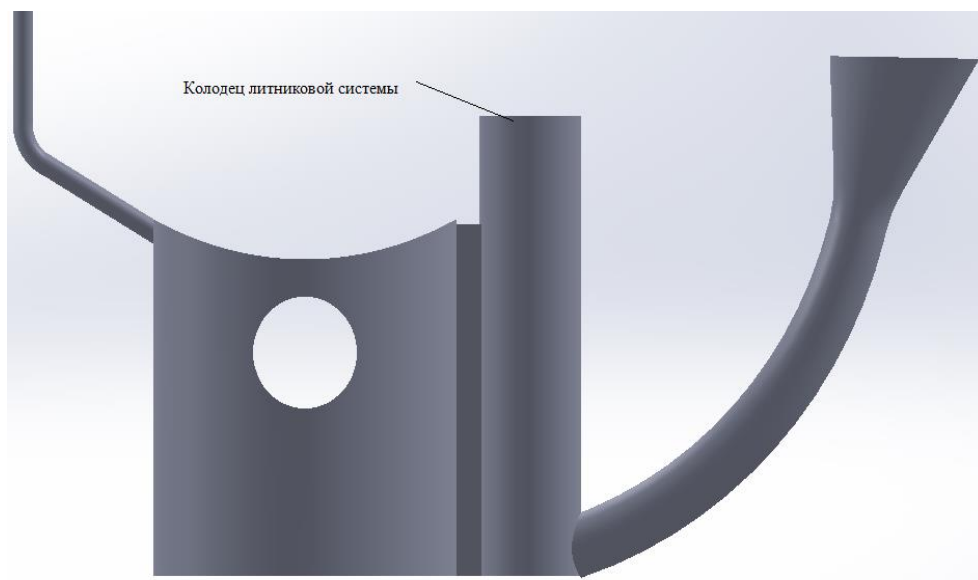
Эскиз отливки «Поршень 4D32» с литниковой системой.
